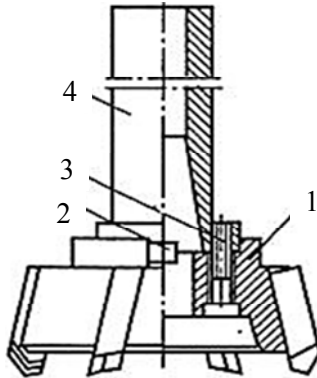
Установка торцовых насадных фрез и головок на шпиндель станка: 1 – фреза; 2 – шпонка; 3 – винт; 4 – шпиндель
